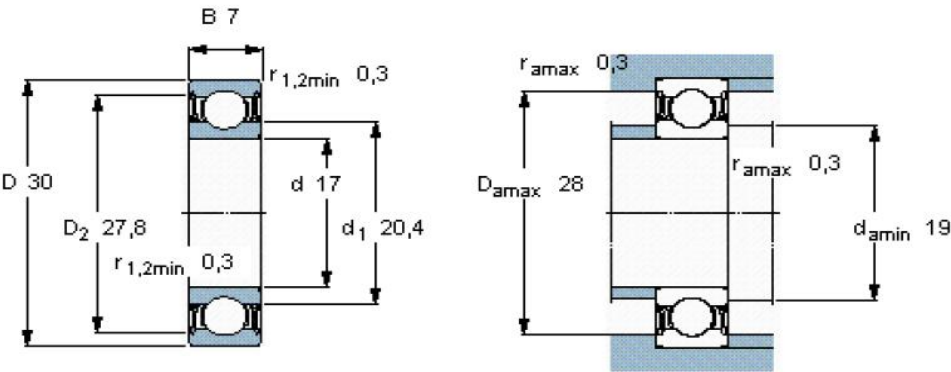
Desenho de definição e esquema de montagem do rolamento 61904-2RZ [19]
